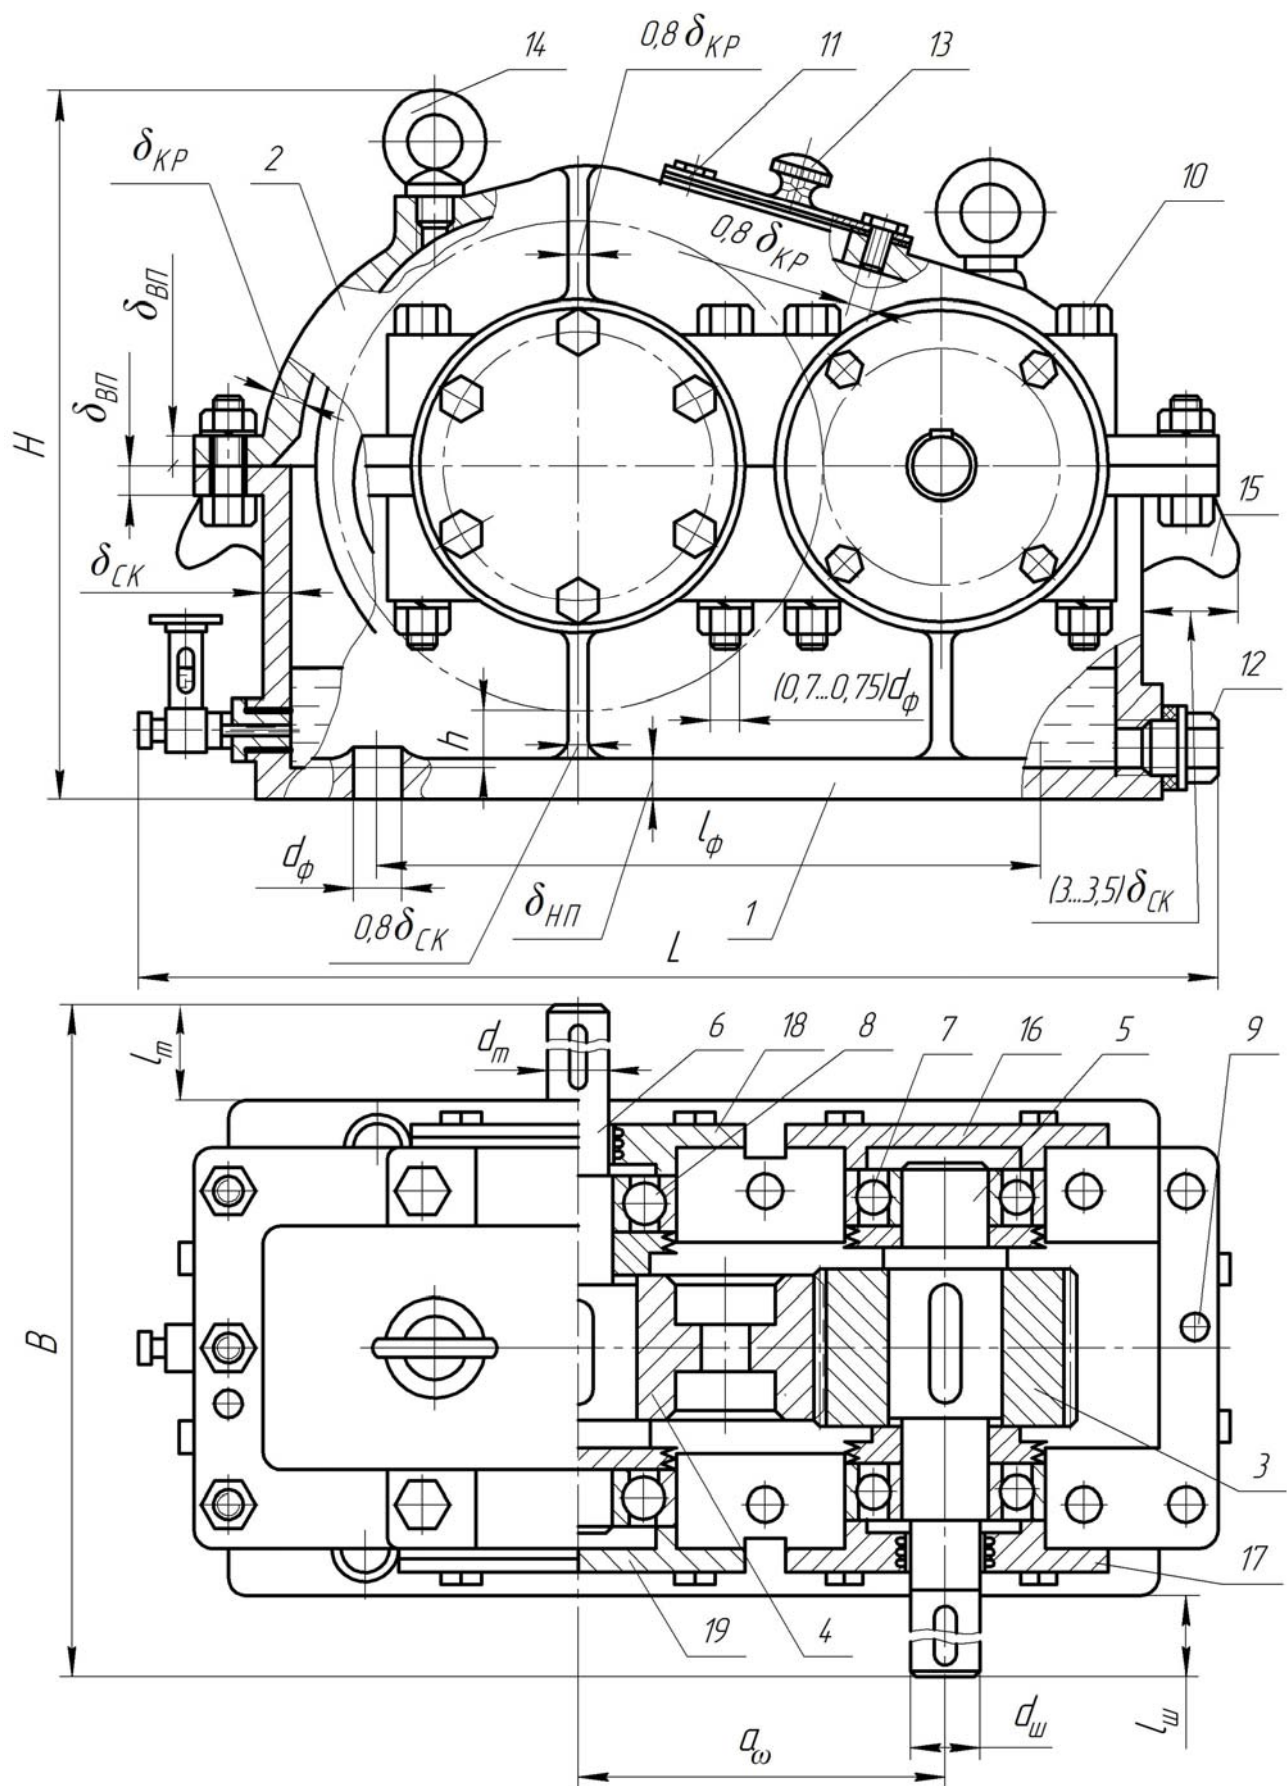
Одноступінчастий редуктор із циліндричними колесами
